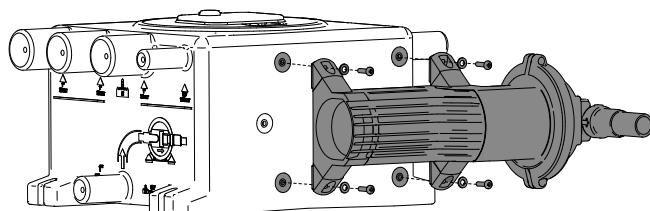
Anschluss der Pumpe Gulper 220 am Grauwassertank
